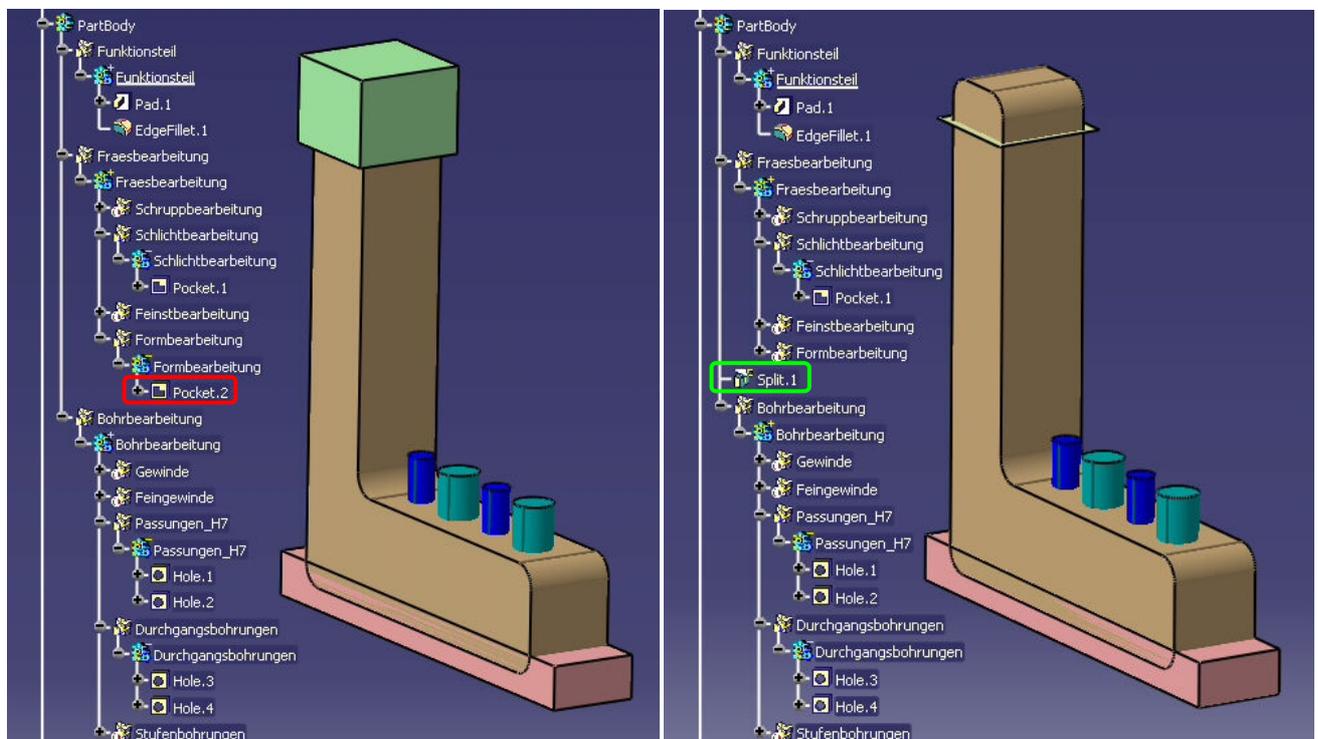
Die Fräs- und Bohrbearbeitung
